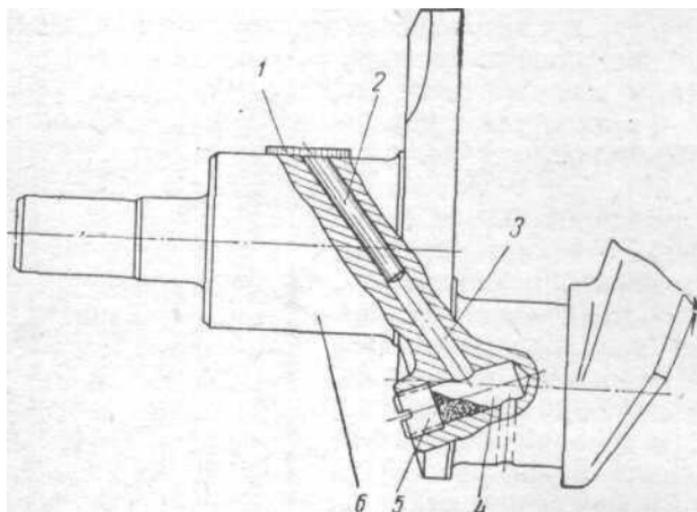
Установка приспособления для выталкивания вкладыша коренного подшипника из постели блока цилиндров:
